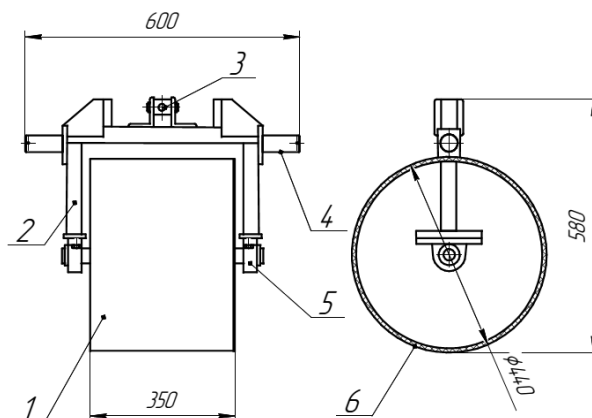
Схема грудкоподрібнюючого катка: 1 – каток; 2 – рамка; 3 – кронштейн; 4 – цапфи; 5 – підшипниковий вузол; 6 – шар гуми
